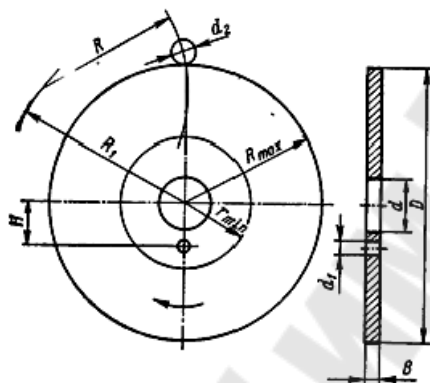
Обозначение размеров заготовки дисковых кулачков
